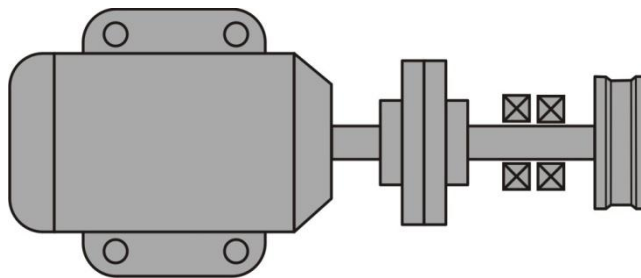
Схема контроля механических потерь в подшипниках быстроходного вала
